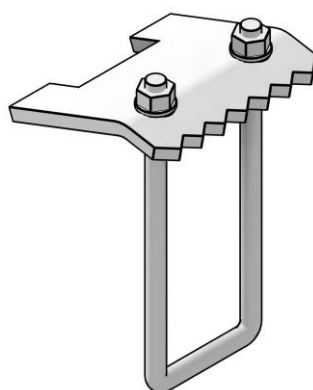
Крепление шпильки к металлической балке при помощи струбцины EFT H
